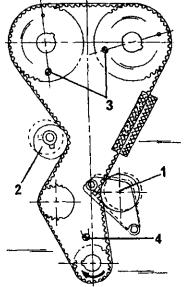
Установка зубчатого ремня на 16клапанном двигателе.
